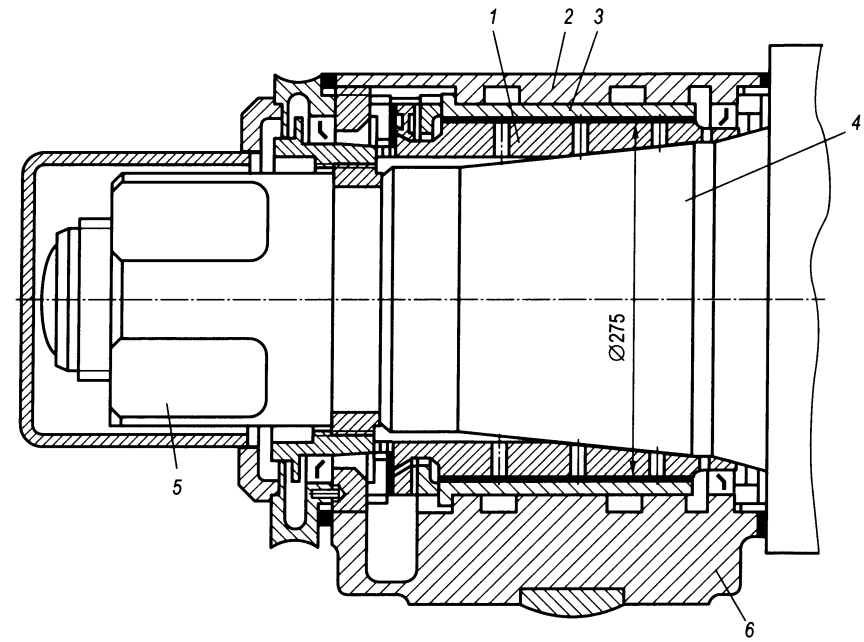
Подшипник вала прокатного стана с упорным фланцем:
